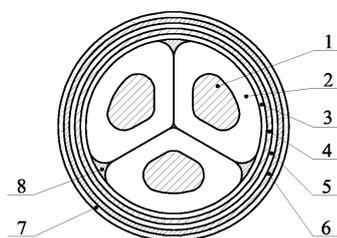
Схема устройства изоляции кабелей до 35 кВ: 1 — жила, 2 — фазная изоляция, 3 — поясная изоляция, 4 — герметичное покрытие, 5 — подушка, 6 — броня, 7 — антикоррозионное покрытие, 8 — наполнитель (джут)
